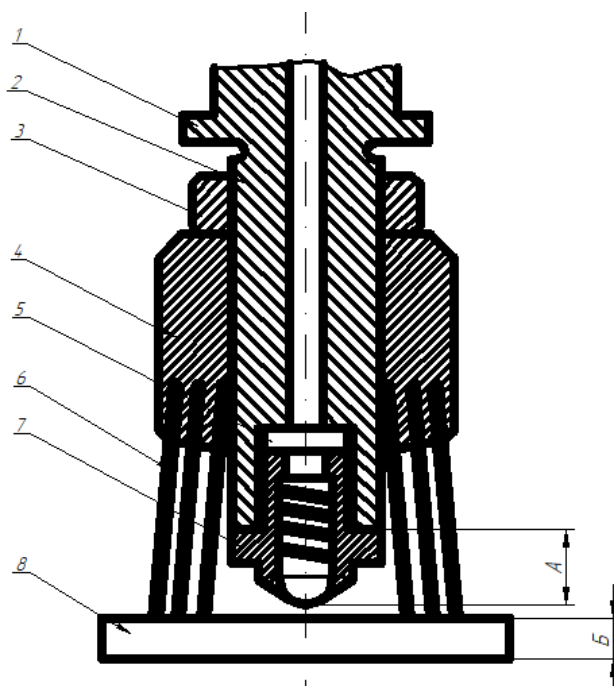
Пристрій для нанесення клею на деталі взуття
